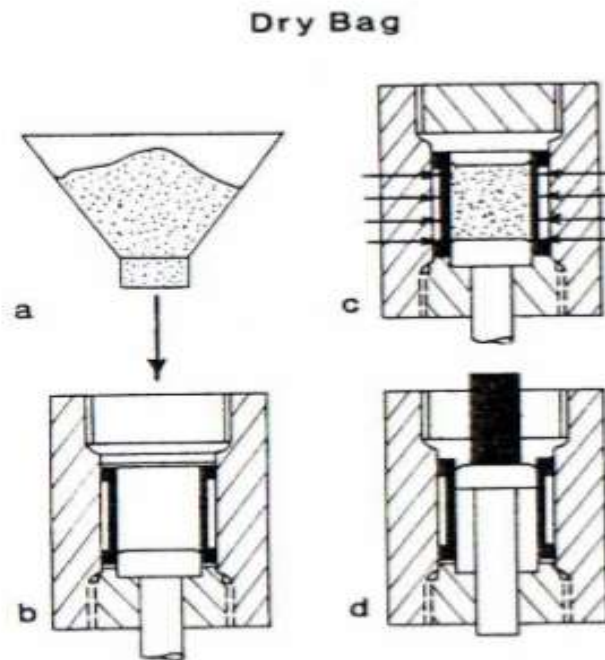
Principe du procédé de pressage en moule sec [2].
